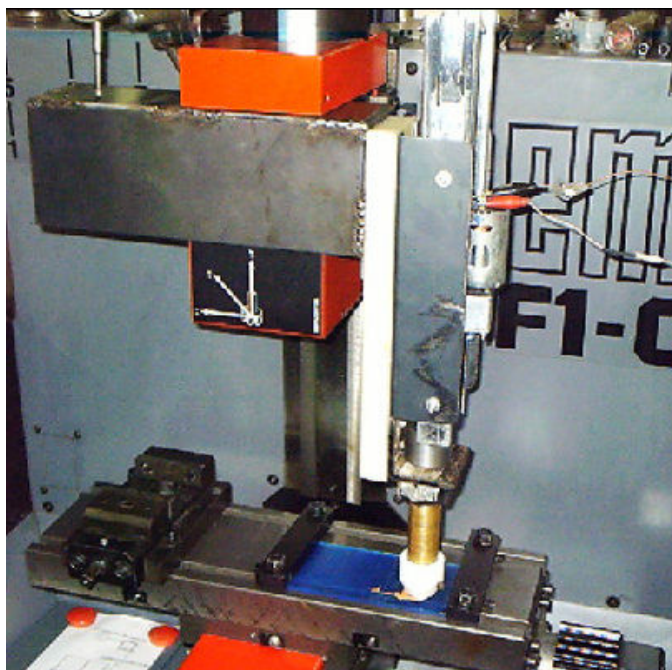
Dispositivo montado na fresadora CNC – (elaborado pelo autor).
